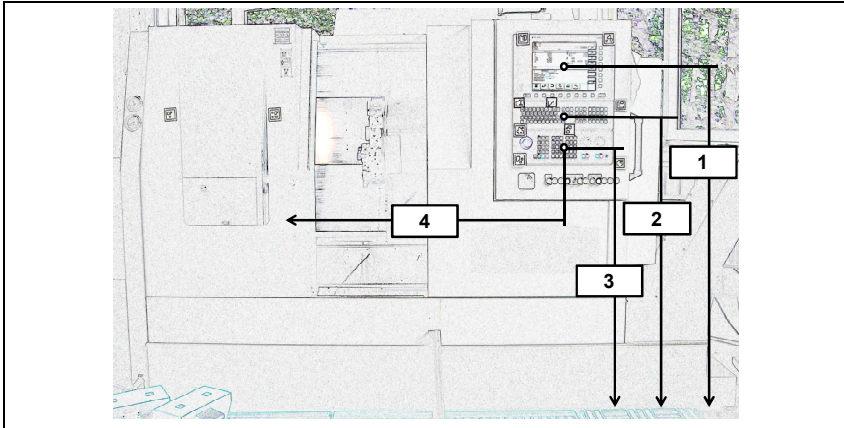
Einige für die Checkliste vorgenommene Messungen an der Werkzeugmaschine: 1, 2, 3 – Höhe der wichtigsten Bedienelemente
